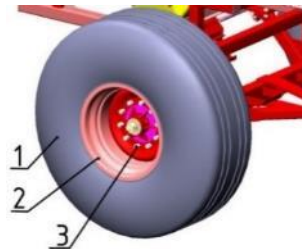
Колеса посівної частини: 1 – шина; 2 – диск; 3 – болт.
